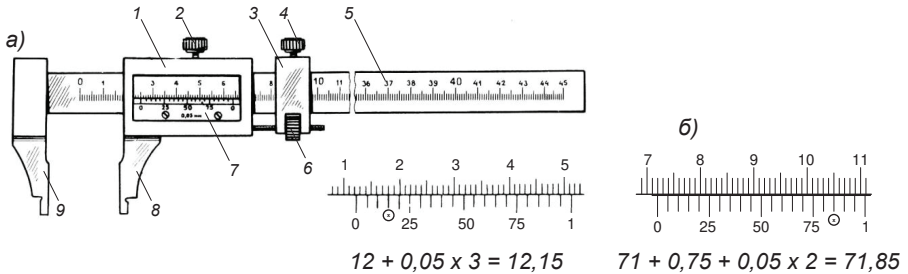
Штангенциркуль ШЦ-Ш: а) устройство; б) примеры отсчета;
